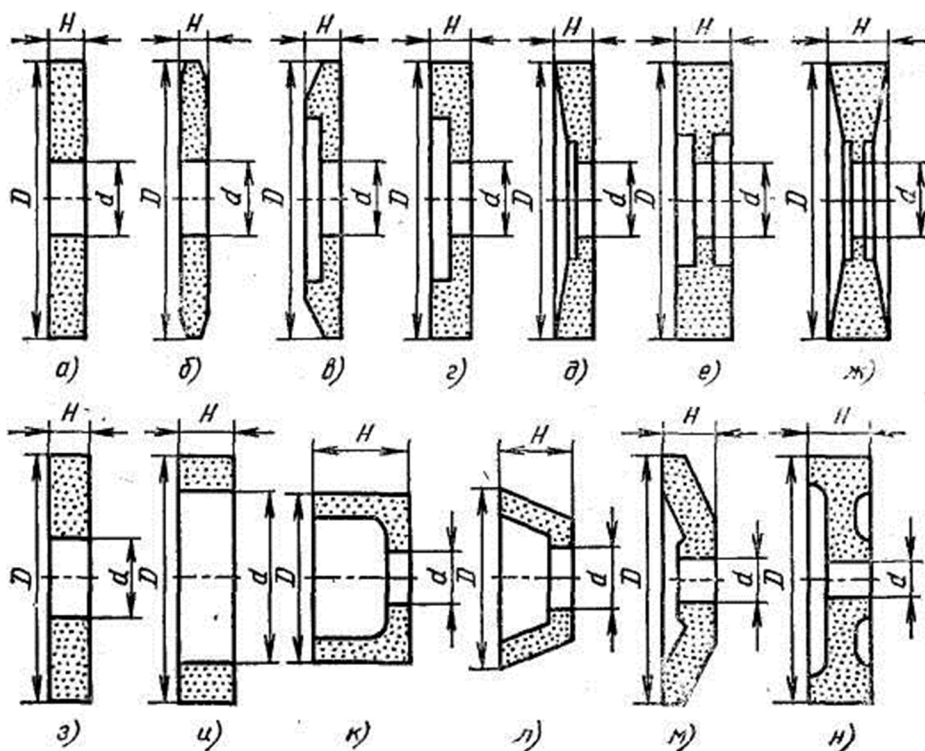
Форма сечений шлифовальных кругов по ГОСТ 2424-83
